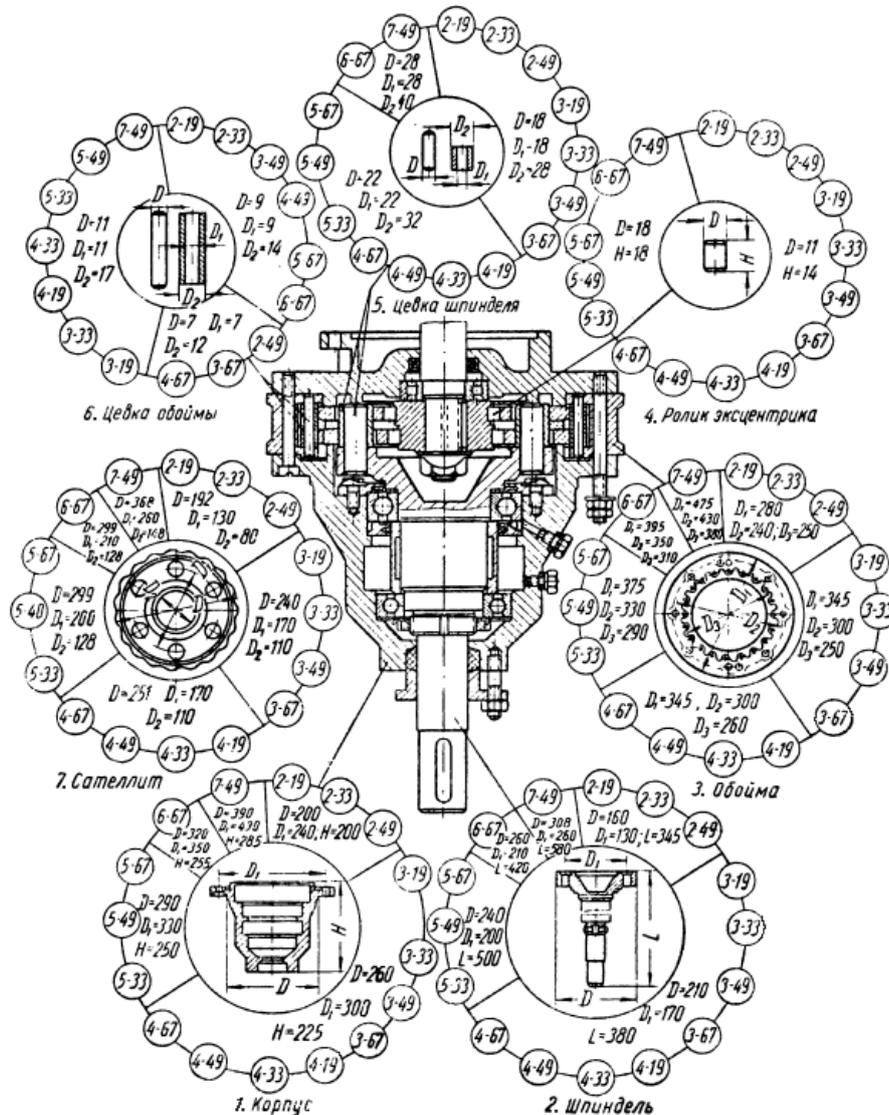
Конструктивно-нормализованный ряд планетарно-цевочных редукторов
